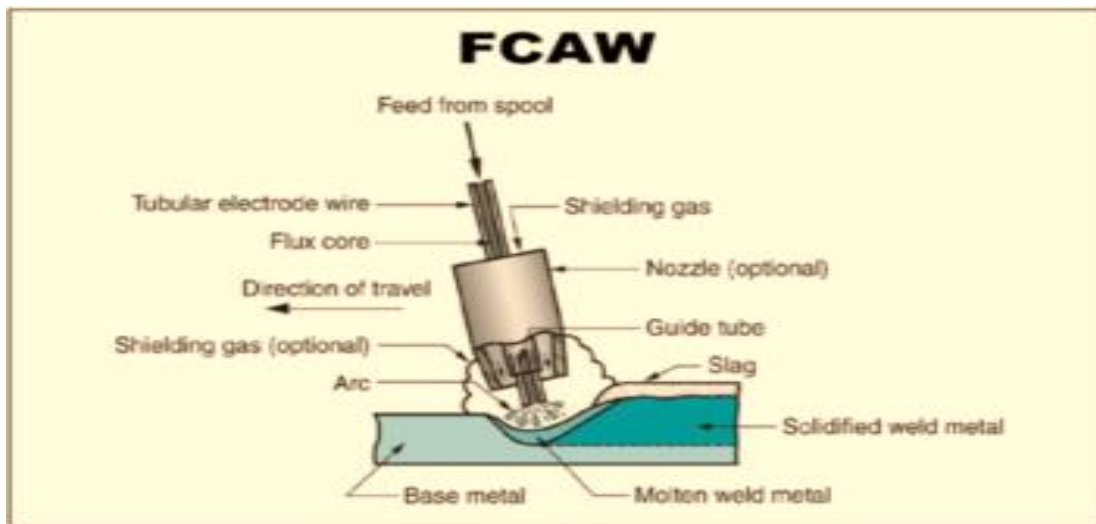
Soudage avec fil fourré et gaz de protection. [28]
